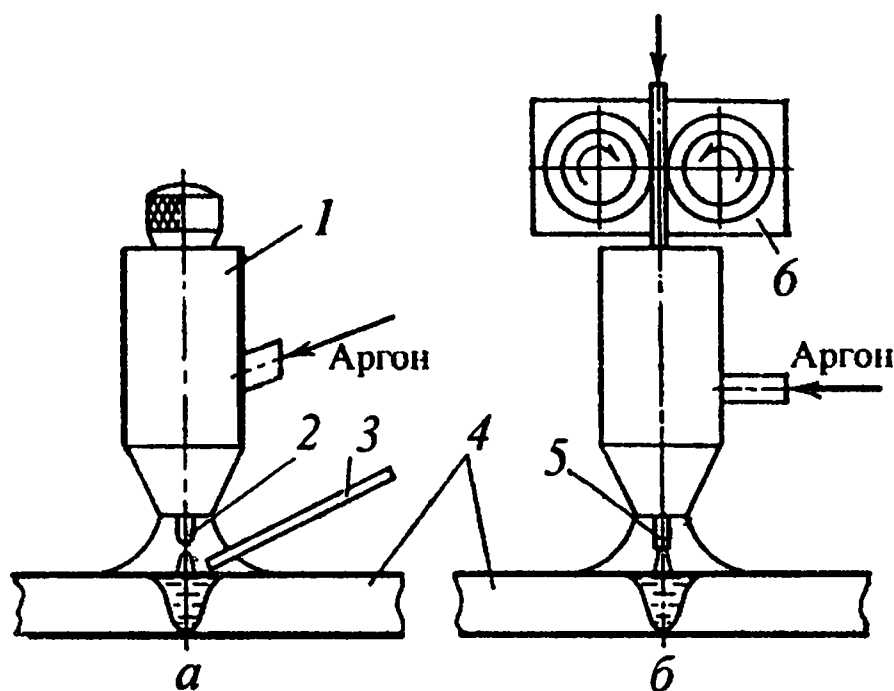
Схема сварки в инертном газе: а — неплавящимся электродом; б — плавящимся электродом; 1 — горелка; 2 — неплавящийся (вольфрамовый) электрод; 3 — присадочная проволока; 4 — свариваемая деталь; 5 — электродная проволока (плавящийся электрод); 6 — механизм подачи
